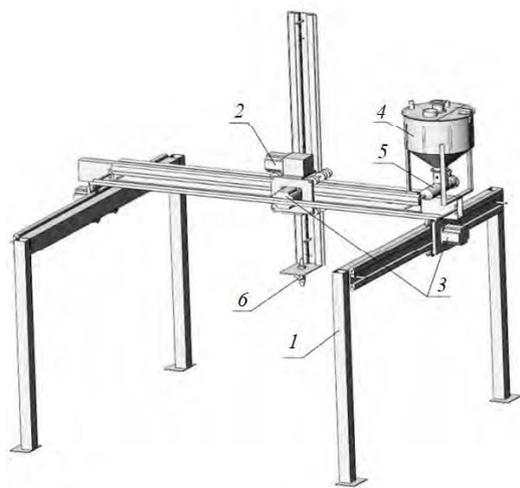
Портальный технологический комплекс послойного синтеза строительных конструкций: 1 – порталная рама; 2, 3 – механизмы перемещения; 4 – дозатор; 5 – подающее устройство; 6 – рабочий орган
